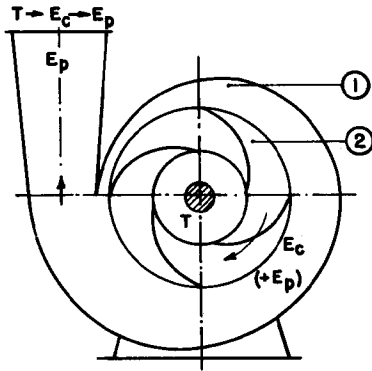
Máquina de fluxo. Bomba centrífuga. 1 — Carcaça; 2 — Rotor.
